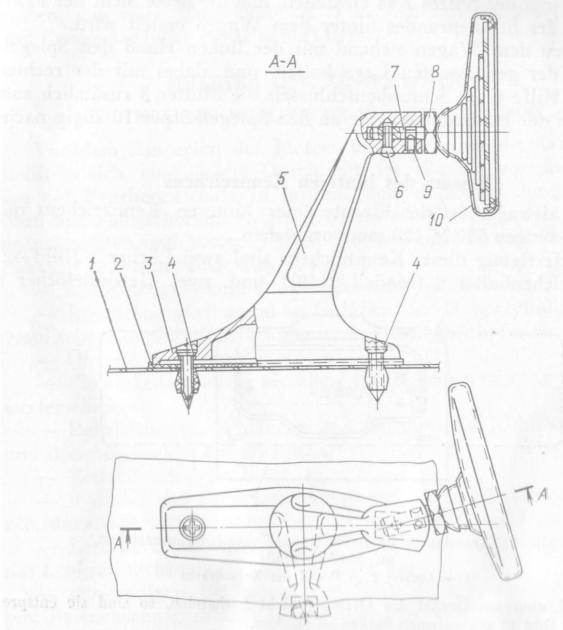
Außenspiegel und dessen Befestigungsteile an Karosserie (Bezeichnung der Positionen siehe im Text)
